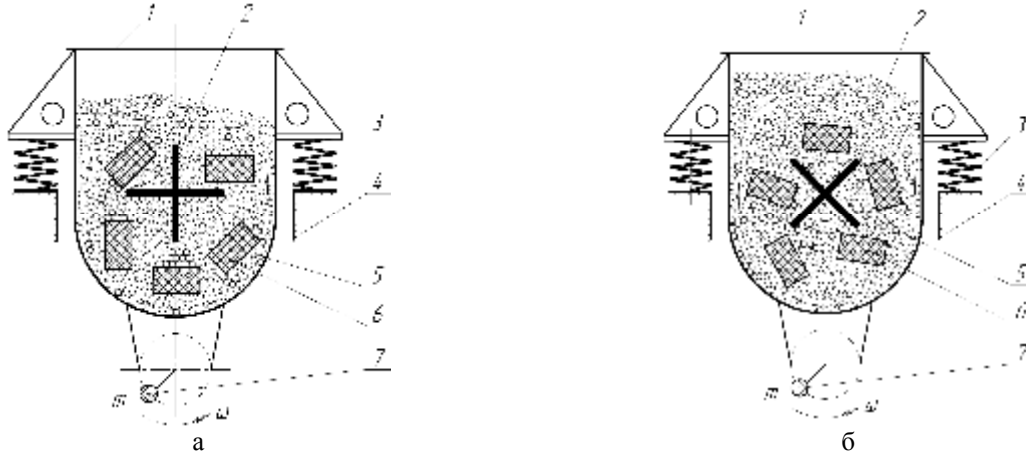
Конструкция виброустановок с прямолинейным дефлектором в резервуаре: 1 – резервуар; 2 - дефлектор; 3 – упругая подвеска; 4 – основание; 5 – рабочая среда; 6 – детали; 7 – вибровозбудитель; (а) – «+» - образным; «X» - образным
